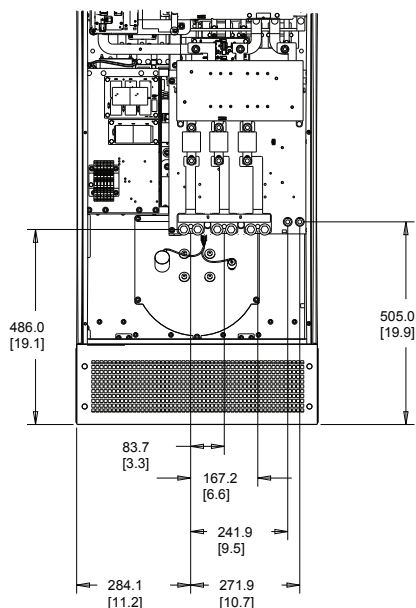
Расположение клемм в корпусе D14 без разъемника
